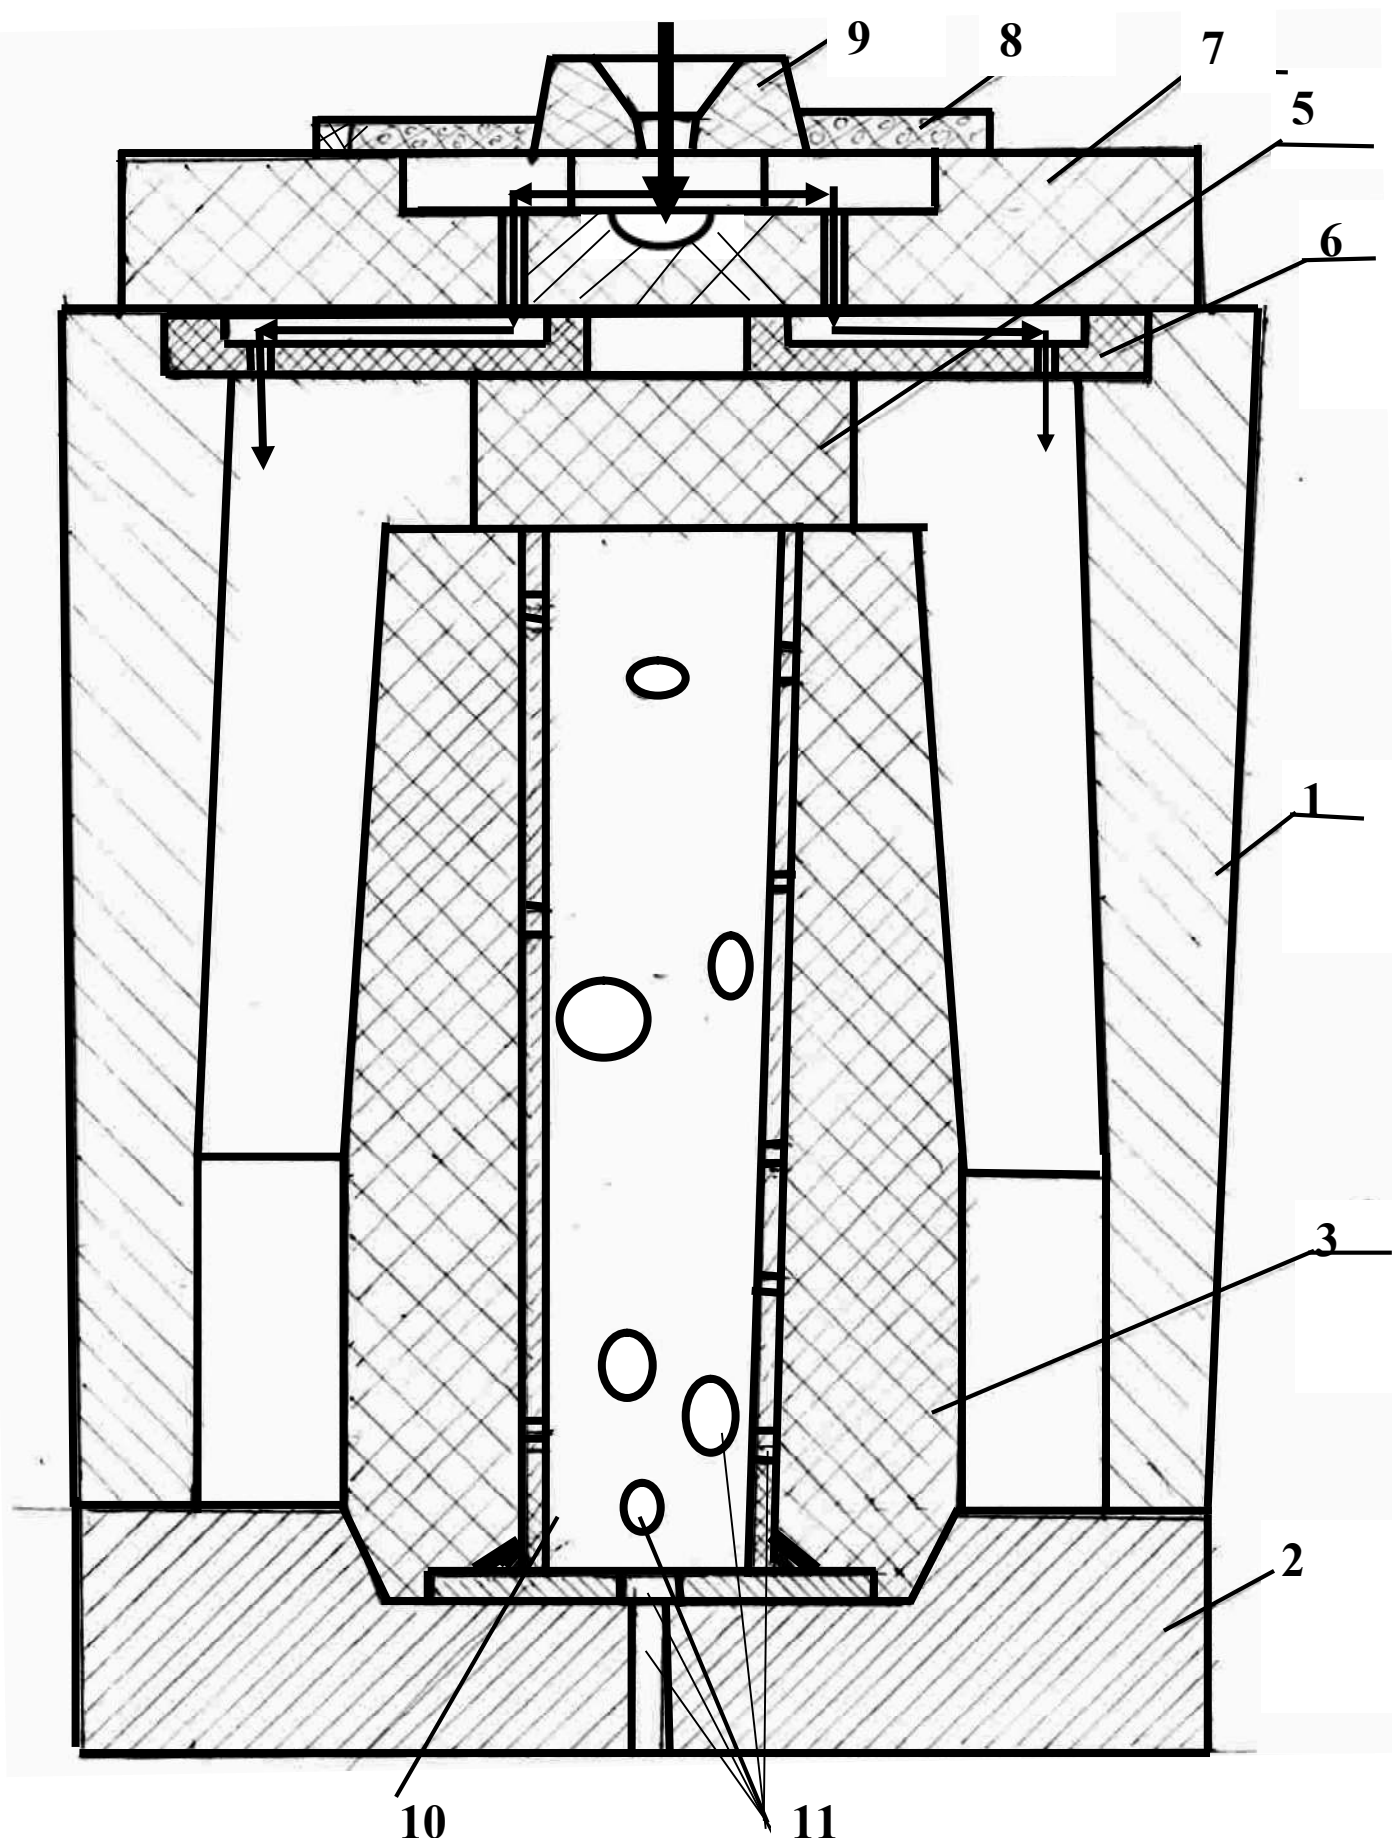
Металлическая форма для отливки стальных изложниц для слитков развесом, т.:
